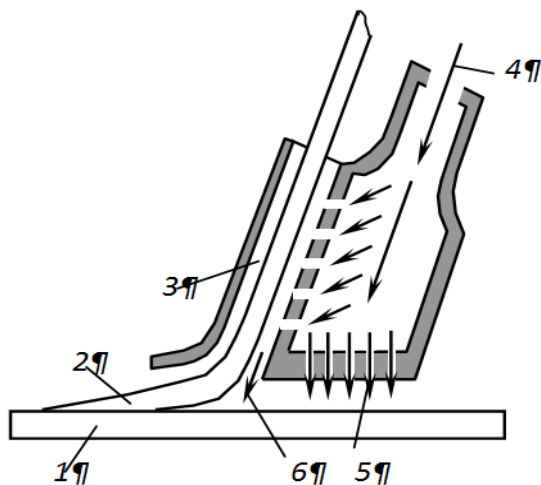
Схема сварки «соплом быстрой сварки»: 1 – свариваемые детали; 2 – присадочный материал (пруток); 3 – камера подогрева присадочного прутка; 4 – нагретый газ; 5 – предварительный нагрев основного материала; 6 – окончательный нагрев основного материала до $T_{св}$
